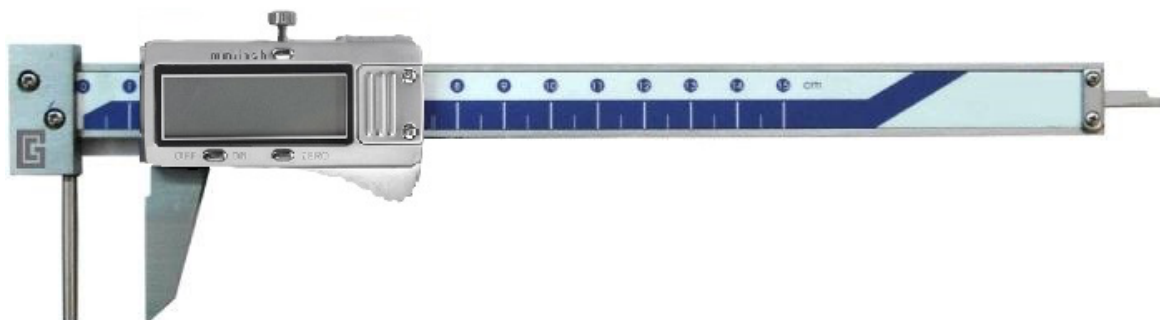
Общий вид штангенциркулей модели ШЦЦС-117
